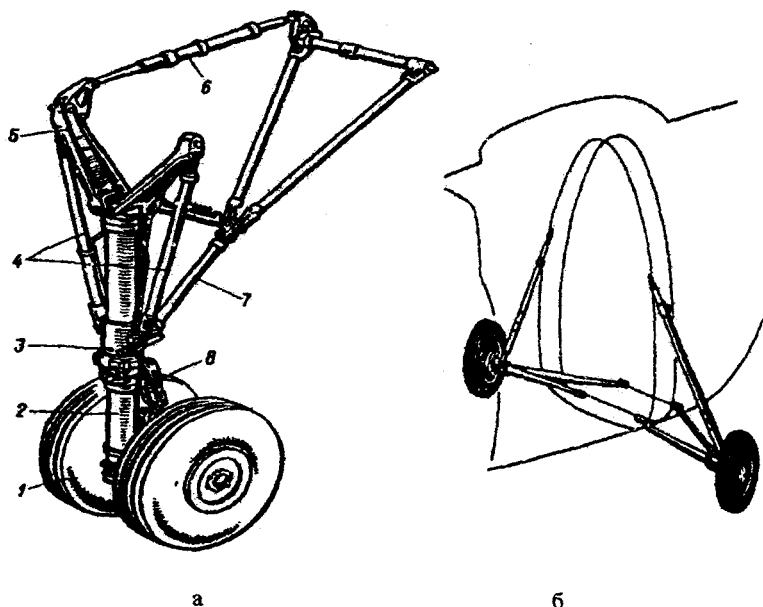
Конструктивно-силовые схемы опор шасси: а – балочно-подкосная; б – ферменная; 1 – колесо; 2 – шток амортизатора; 3 – амортизатор; 4, 7 – подкосы; 5 – траверса; 6 – гидроцилиндр уборки и выпуска опоры; 8 – двузвенник (шлиц-шарнир)
